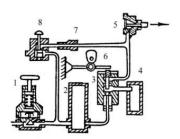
Пневмосистема пневматической ткацкой машины [4]: 1 — редукционный клапан, 2 — главный ресивер, 3 — перепускной клапан, 4 — вспомогательная камера, 5 — форсунка, 6 — управляемый кулачок, 7 — обратный клапан, 8 — ножной вентиль
